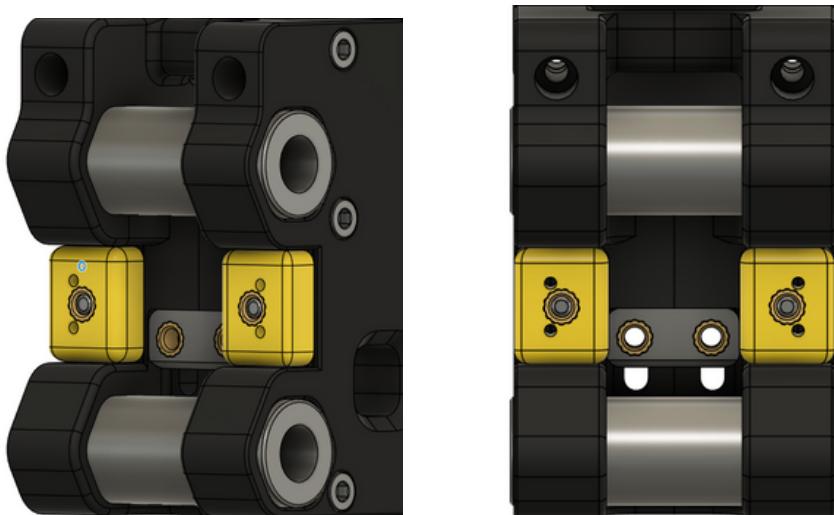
Pieza resultante con rodamientos y fija con tornillos.
